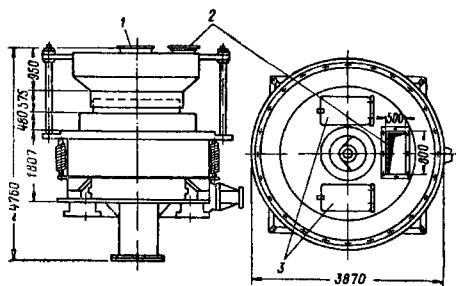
Укрытие загрузочной части конусной дробилки
